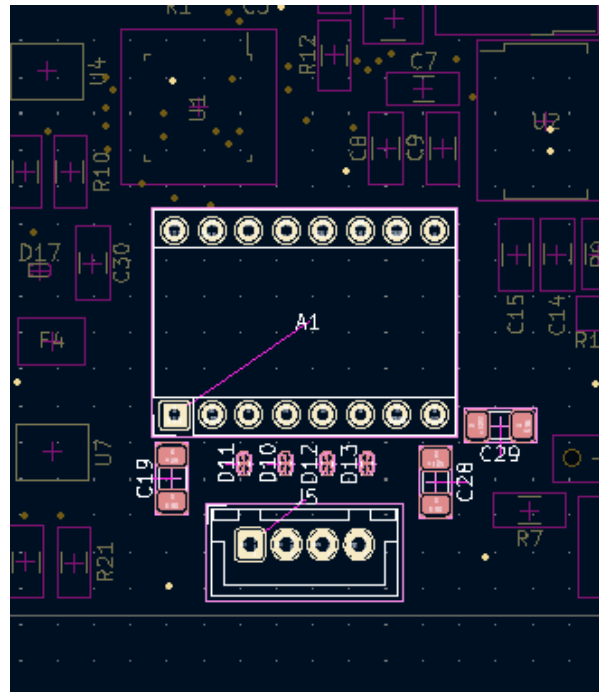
Subsistema Control Motor Paso a Paso PCB Principal
